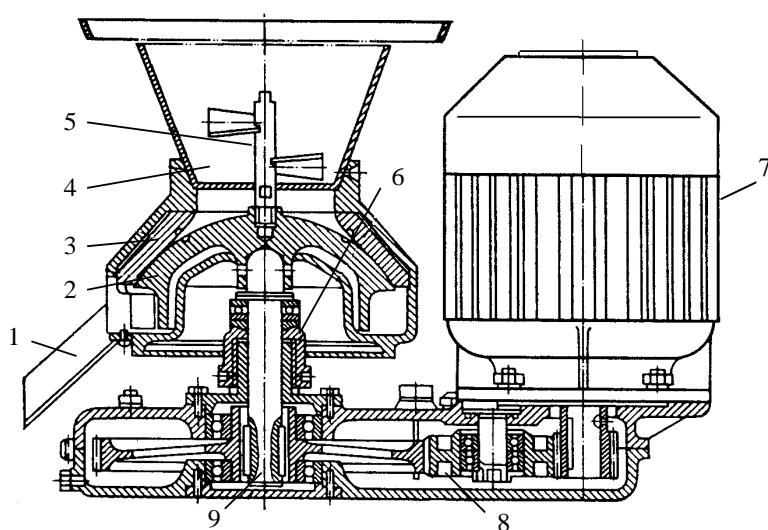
Жерновая краскотерка: 1 – лоток; 2, 3 – жернова; 4 – бункер; 5 – стержень; 6 – стакан; 7 – электродвигатель; 8 – редуктор; 9 – вал вертикальный
